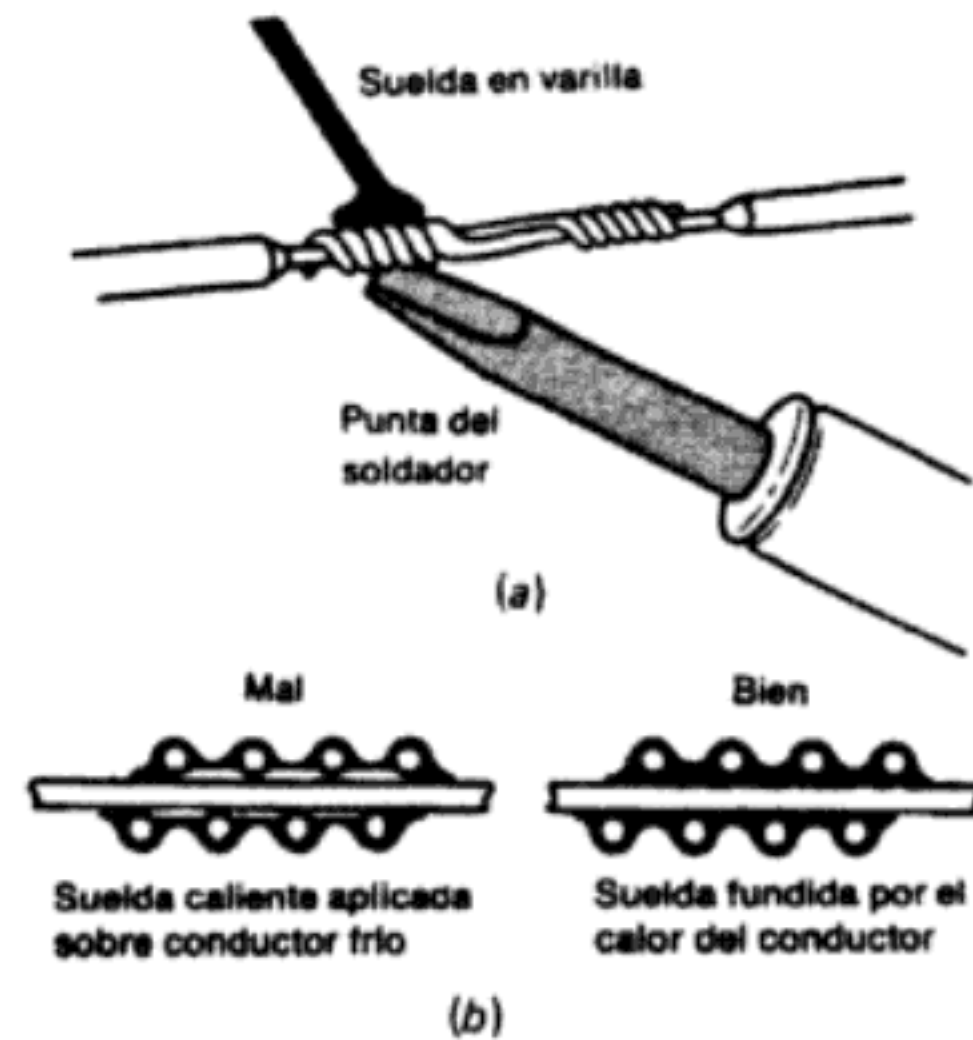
Aplicación de la suelda. (a) La suelda se aplica a la unión caliente, no al soldador. (b) En las uniones soldadas correctamente, la suelda fluye alrededor de los conductores; y, una vez enfriada, presenta un aspecto brillante.
